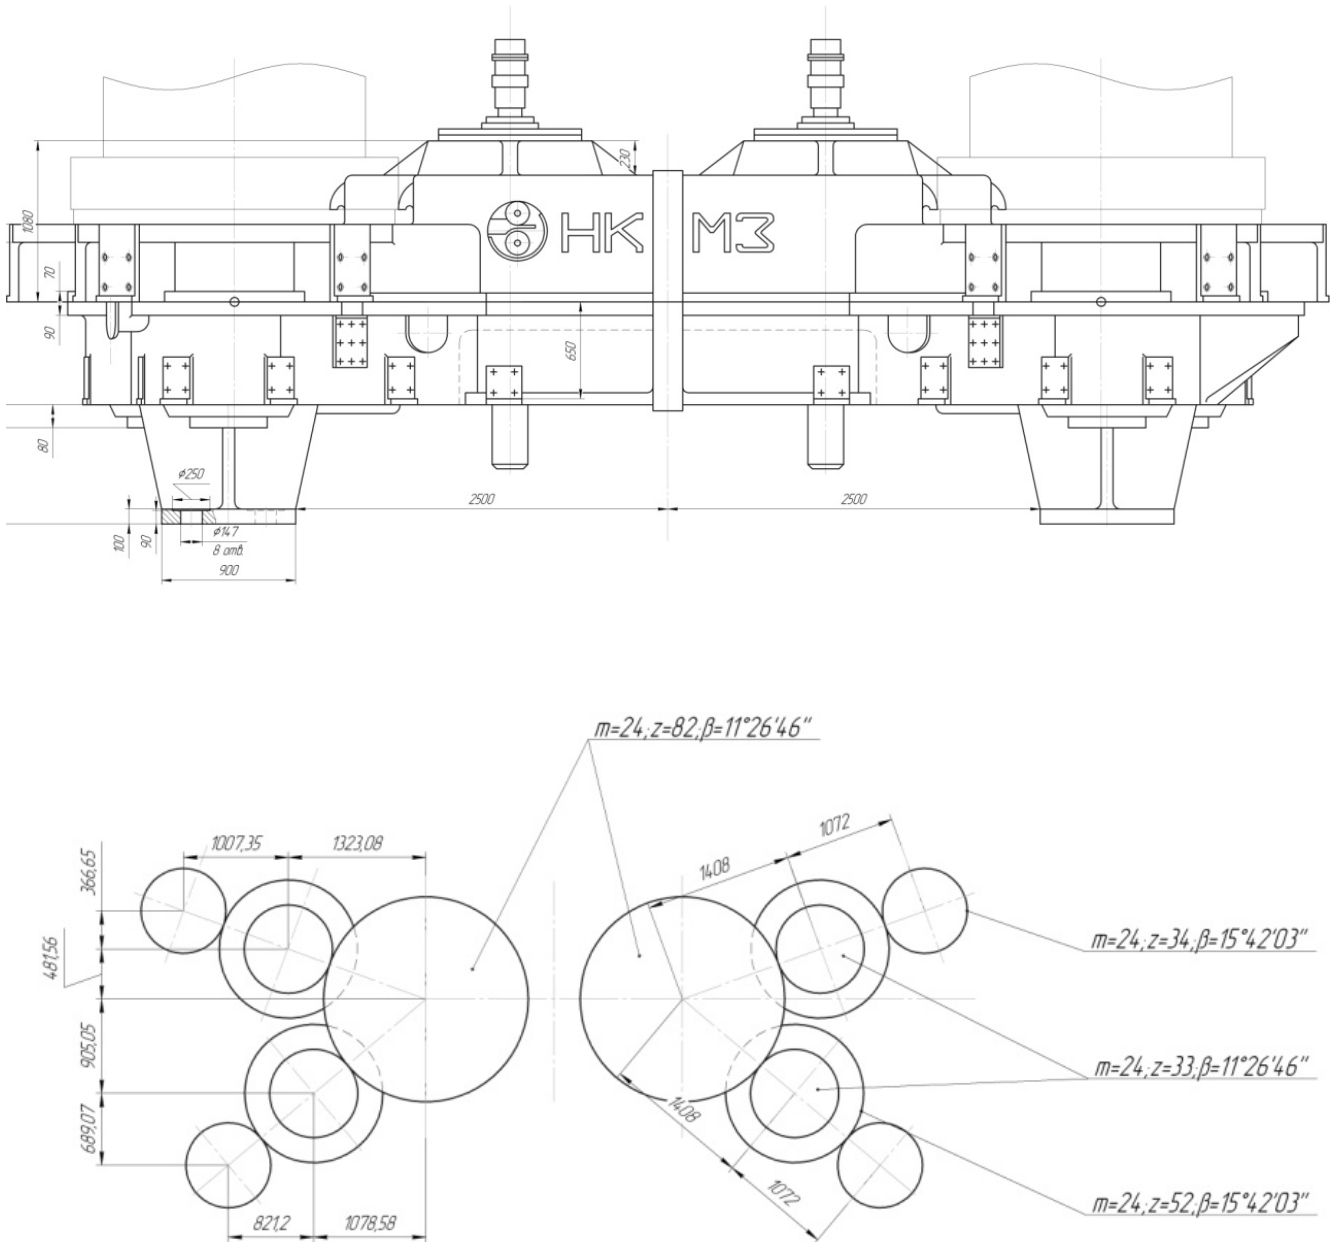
Загальний вид і кінематична схема зачеплення редуктора приводу вертикальних валків реверсивного стану “Слябінг 1150”.
